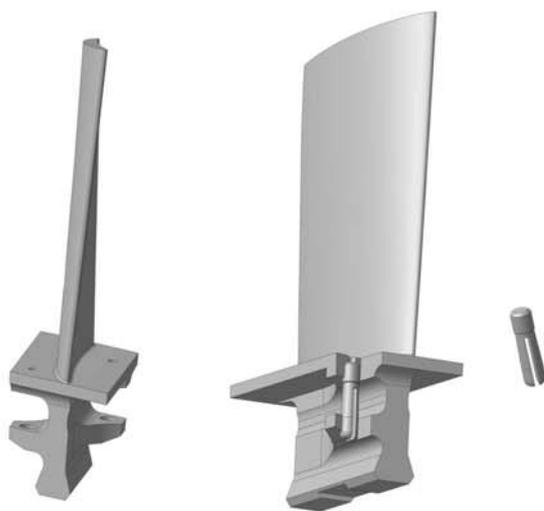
Рабочая лопатка 8-й ступени компрессора с демпфером штифтовым (оригинальная конструкция)
